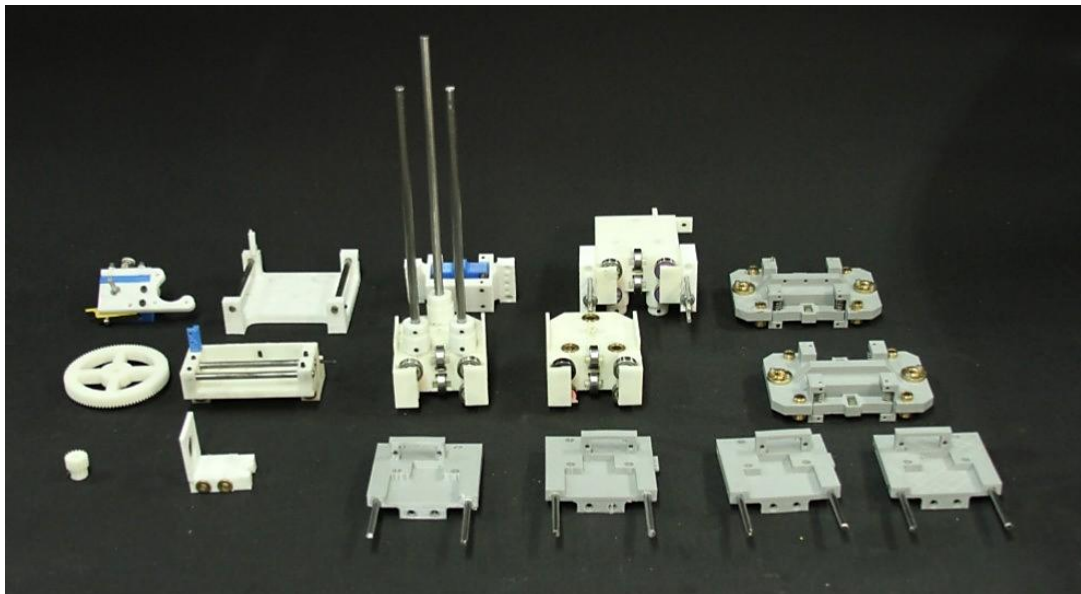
Despiece de componentes. Se acoplaron bujes, ejes y tuercas a cada componente.
